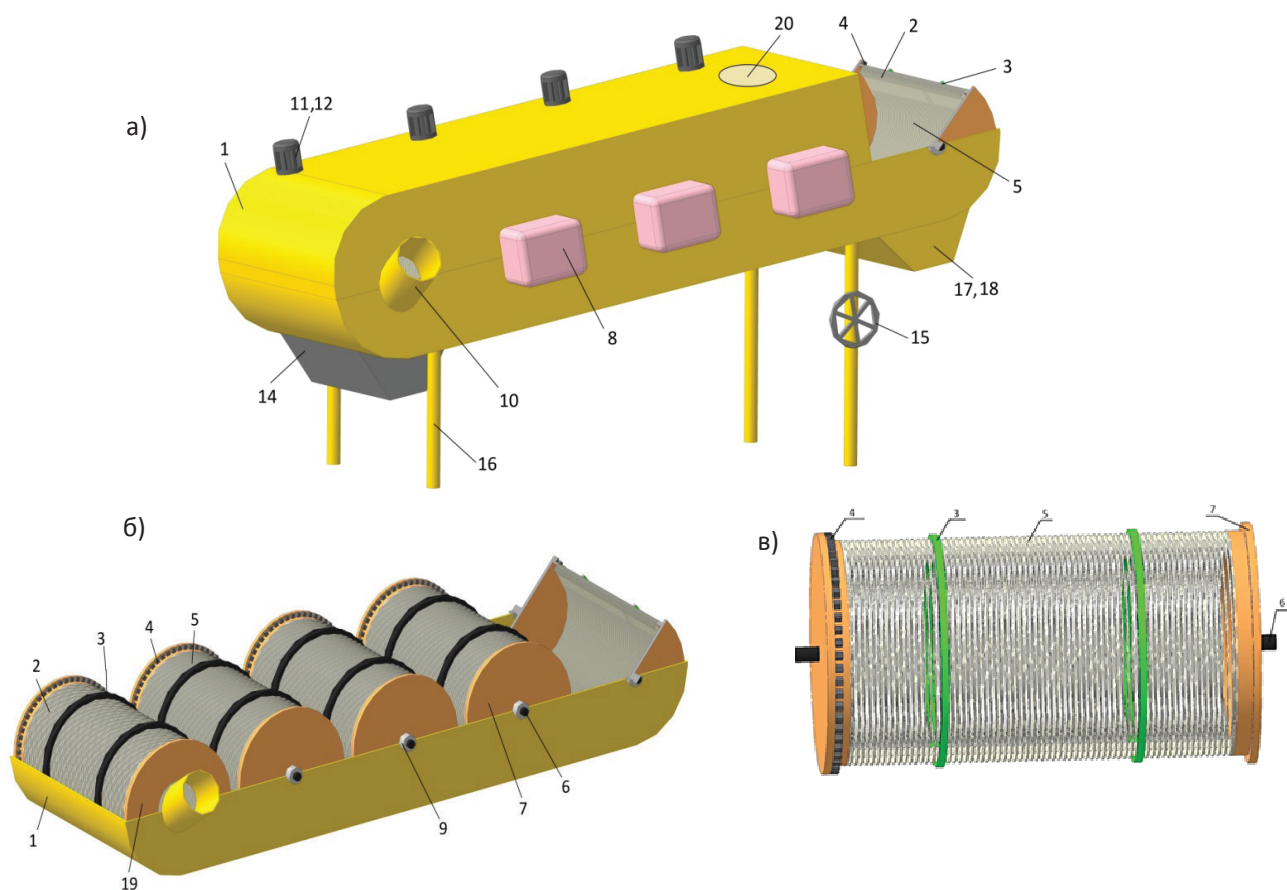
Сверхвысокочастотная установка с цилиндрическими барабанами-резонаторами для непрерывного режима работы: а) общий вид в разрезе; б) цилиндрический барабан из витков
